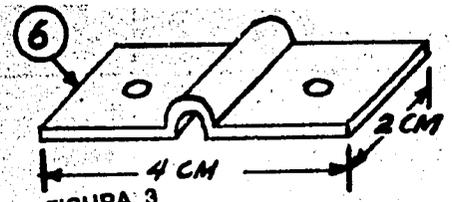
DETALLE DE LA PIEZA 6, ANCLAJE DE LA VARILLA ALIMENTADORA, LA PARTE 7, VARILLA ALIMENTADORA
